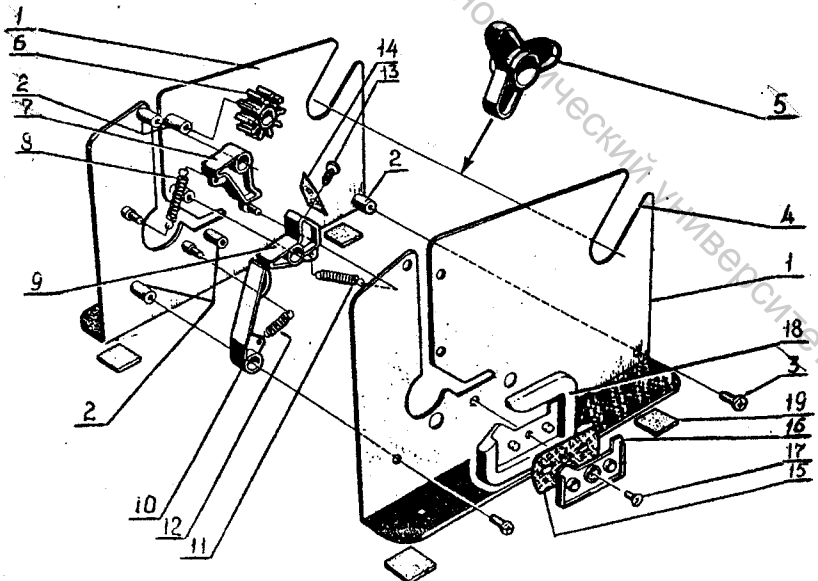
Приспособление для заклеивания полиэтиленовых пакетов
